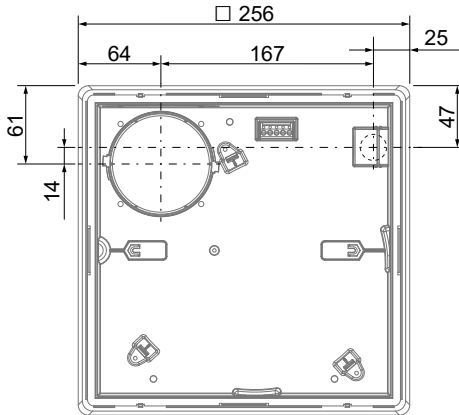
Maßzeichnung – Kabeldurchführung Abluftventilator Taris AP
